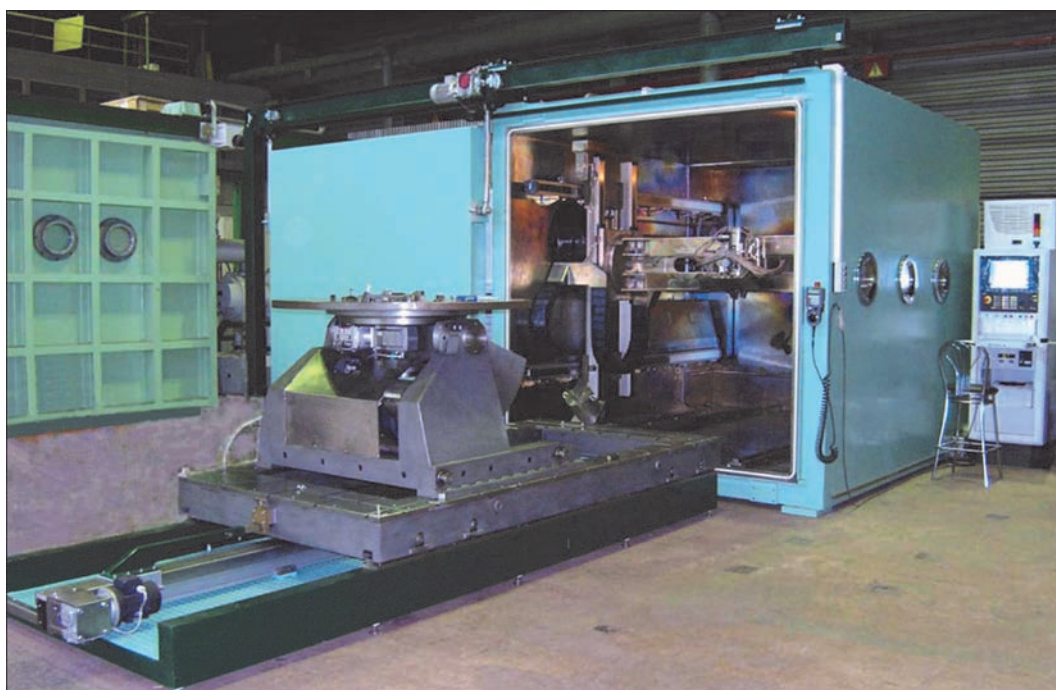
Типова середньогабаритна камера з мобільною зварювальною гарматою та викатний робочий стіл
